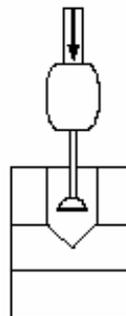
Das Werkzeug seitwärts in Richtung Bohrungswand bewegen bis sich die Achse des Werkzeughalters im Durchmesser der auszuführenden Kreisbewegung befindet.
